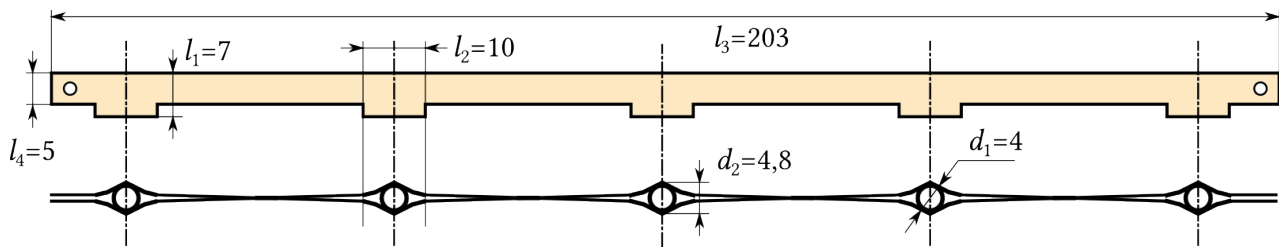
Сборочный чертеж контактной пластины сетевого фильтра
